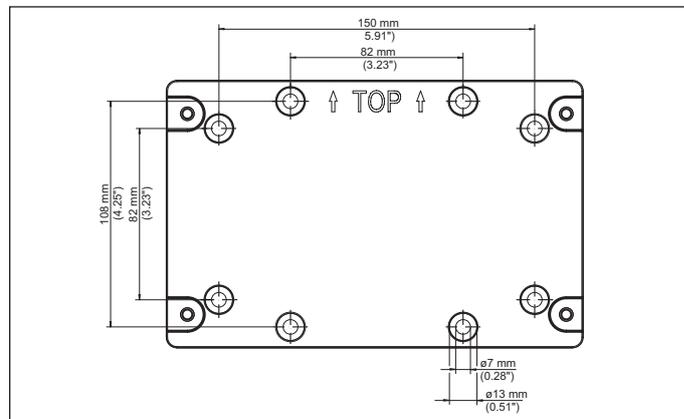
Placa de montaje para montaje en pared (VEGAMET 861, 862)
